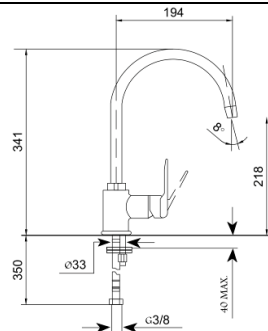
, Dibujo técnico grifo, TEKA ref. 5399512
